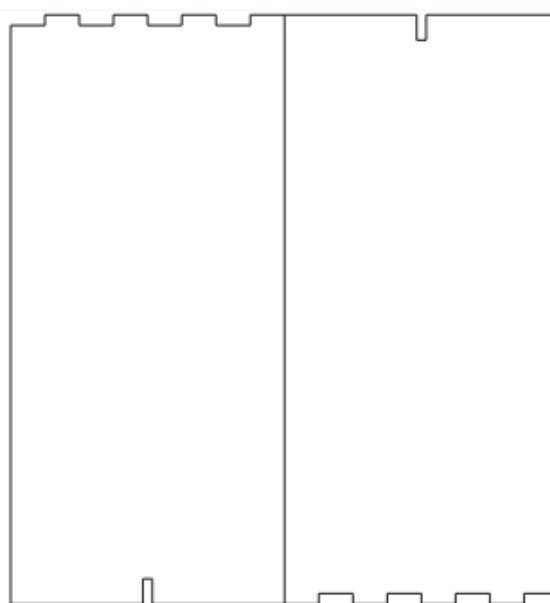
Креслення для виготовлення платформи для макета
